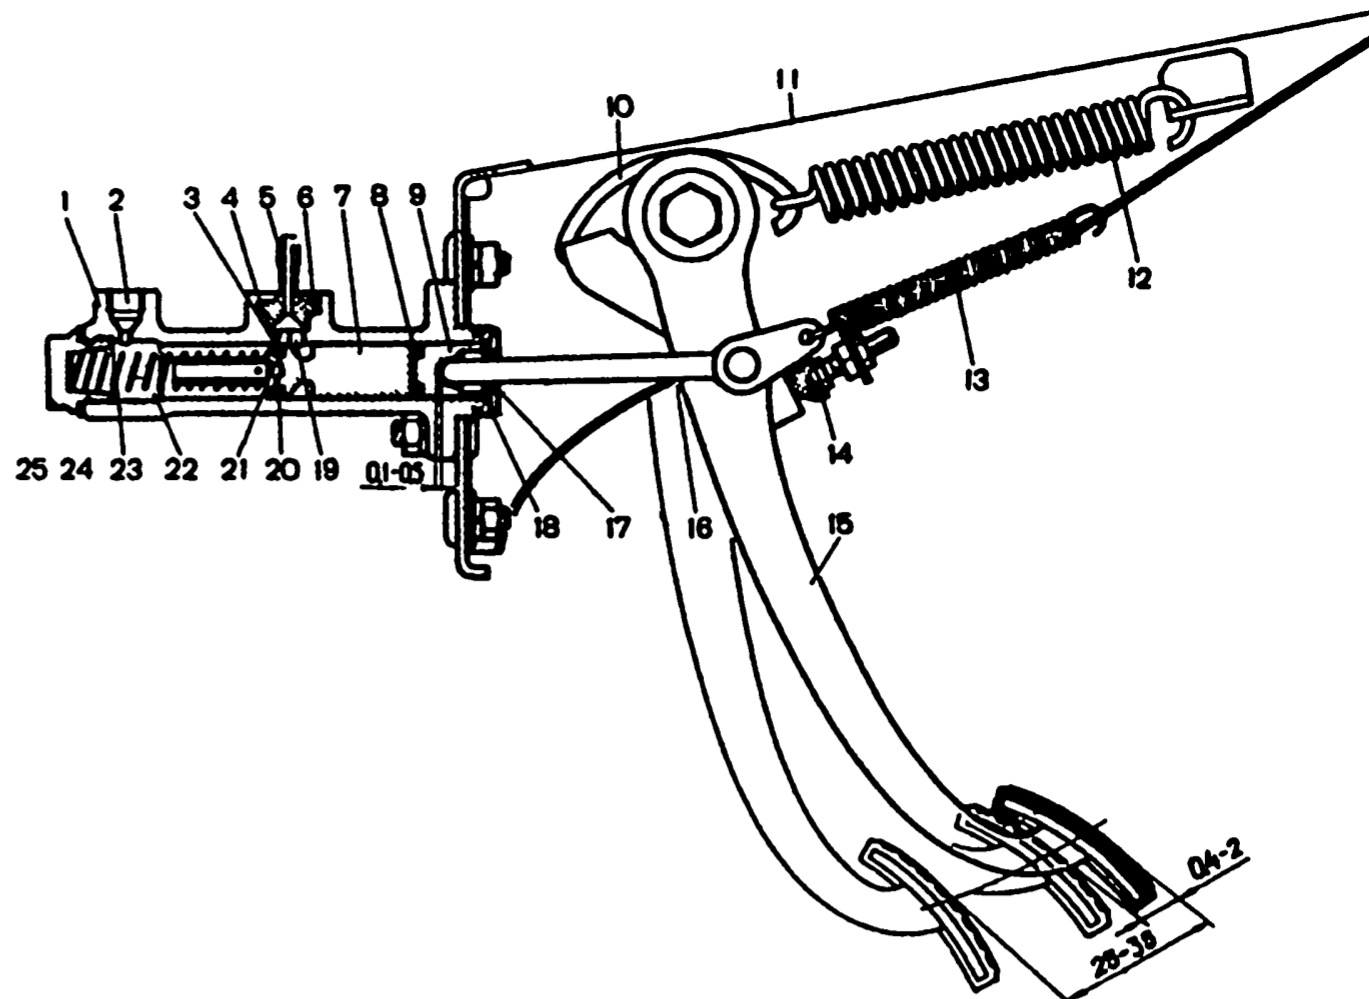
Педаль и главный цилиндр привода сцепления: 1 - корпус главного цилиндра; 2 - гнездо; 3 - перепускное (компенсационное) отверстие; 4 - прокладка штуцера; 5 - штуцер; 6 - стопорная пружинная шайба; 7 - поршень главного цилиндра; 8 - уплотнительное кольцо; 9 - поршень толкателя; 10 - крючок; 11 - кронштейн педалей сцепления и тормоза; 12 - пружина сервопривода педали сцепления; 13 - оттяжная пружина педали сцепления; 14 - ограничитель хода педали сцепления; 15 - педаль сцепления; 16 - толкатель поршня; 17 - защитный колпачок; 18 - стопорное кольцо; 19 - впускное отверстие; 20 - уплотнительное кольцо (кольцевой клапан); 21 - перепускное отверстие поршня; 22 - рабочая полость цилиндра; 23 - пружина; 24 - прокладка; 25 - пробка
